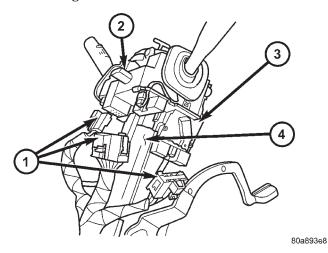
MAZO DE CABLEADO EN LA COLUMNA
